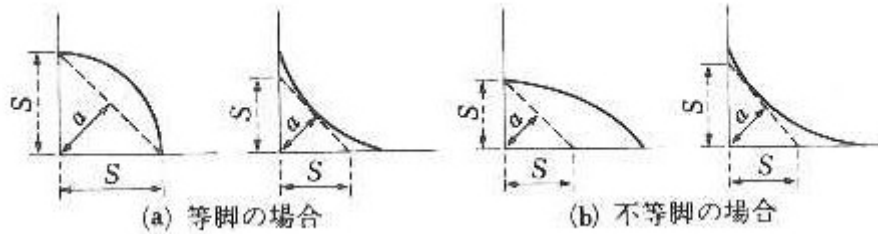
すみ肉溶接の理論のど厚
